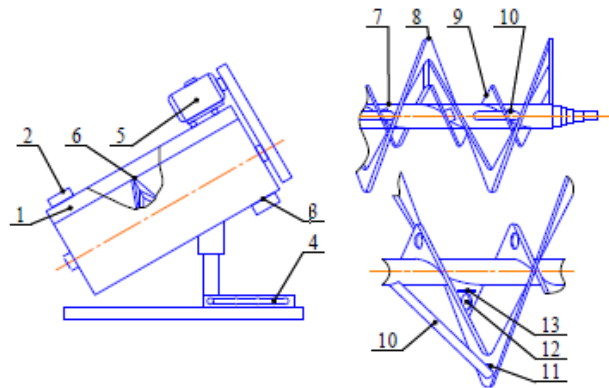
Змішувач за патентом № 2008082: 1 – корпус; 2, 3 – завантажувальний і розвантажувальний патрубки; 4 – рама; 5 – привід; 6 – змішувальний робочий орган; 7 – приводний вал; 8, 9 – зовнішня і внутрішня шнекові стрічки; 10 – жолоб; 11, 12, – отвори; 13 – пластина
